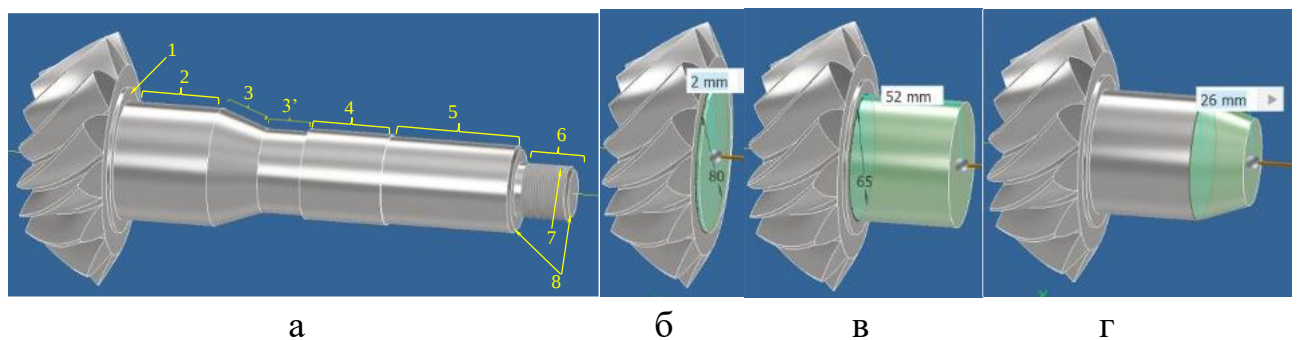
3-D модель вал-шестерні: 1 – упорний буртик; 2, 4 – місця для посадки підшипників; 3, 3' – елементи вала; 5 – циліндр для нарізки шліців; 6 – наріз; 7 – отвір; 8 – фаски
